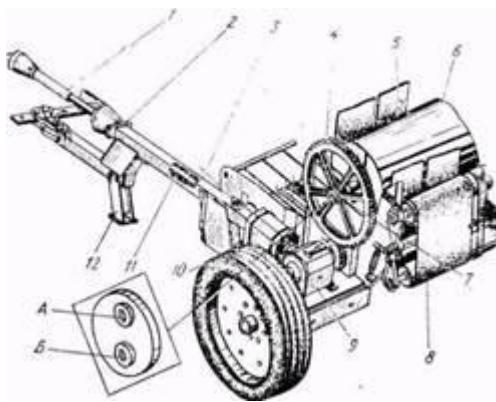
Сница с карданной передачей: 1 - вал карданный; 2 - опора; 3 - сница; 4 - колесо зубчатое; 5 - ремень прессующий; 6 - барабан, 7 - эксцентрик; 8 - транспортер; 9 - редуктор; 10 - кожух муфты; 11 - вал промежуточный; 12 - опора сницы. А и Б - отверстия эксцентрика
